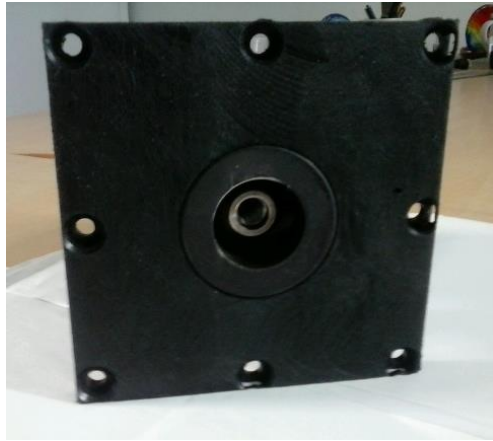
Photographie du fond de chambre usiné en polyéthylène de couleur noire. La surface de la pièce est rendue rugueuse pour atténuer les réflexions.
